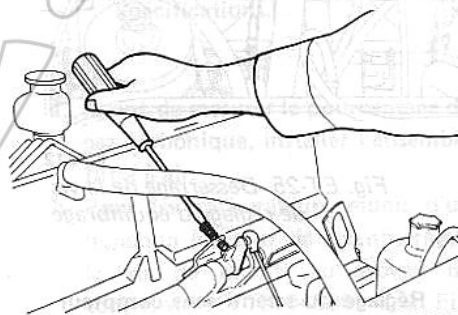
Réglage de la vis de réglage de ralenti accéléré
